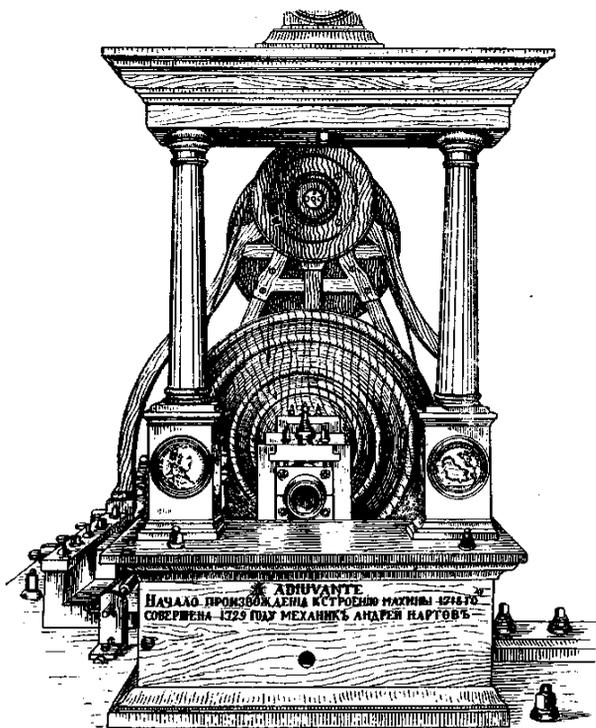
Колоннада большого токарно-копировального станка Нартова 1718—1729 гг.
